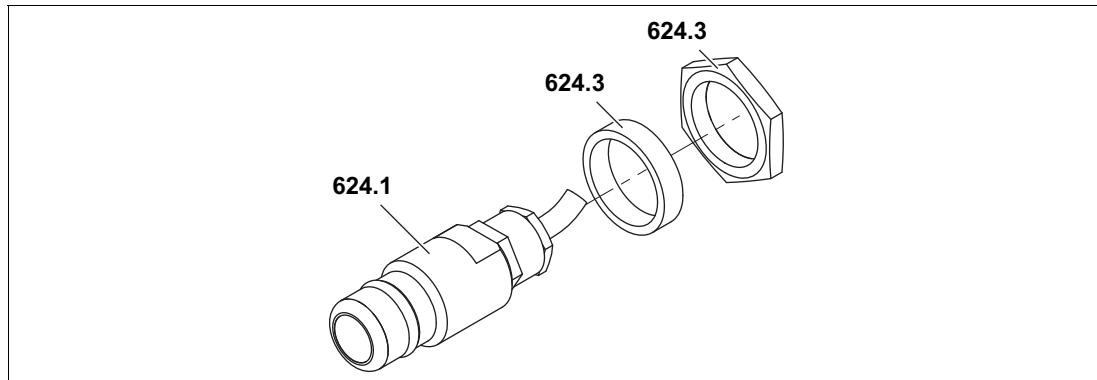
Explosionszeichnung BEG 06/BEG 06A
